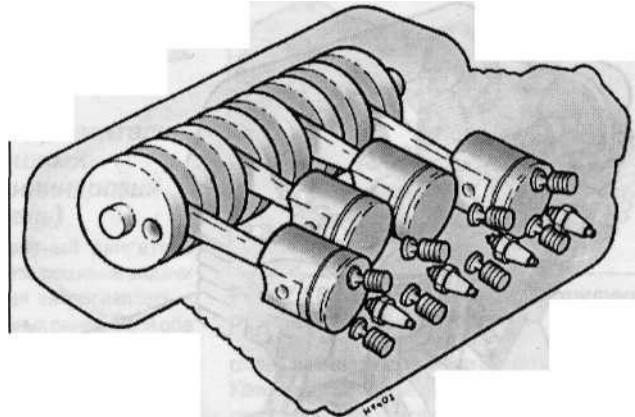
Рядный четырехцилиндровый двигатель горизонтального расположения
